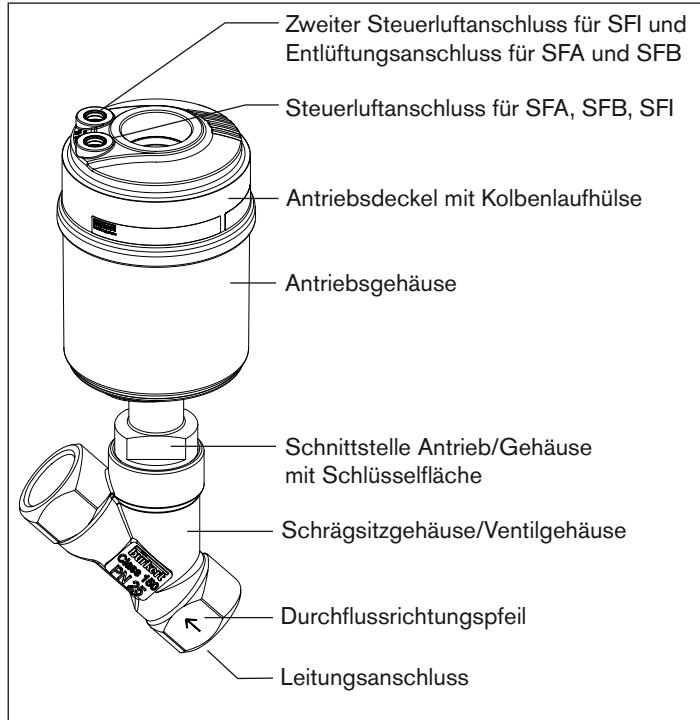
Schrägsitzregelventil Typ 2300, Aufbau und Beschreibung
